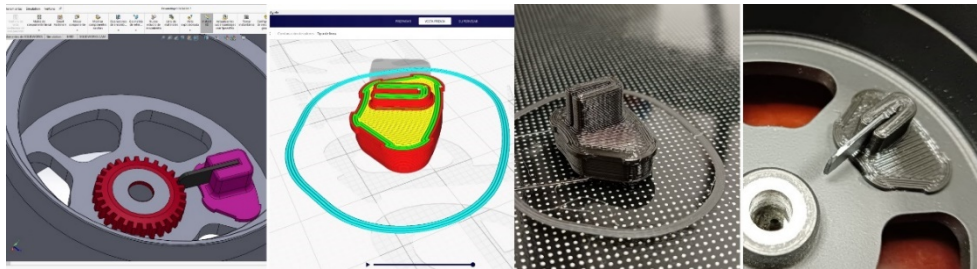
Del diseño a la fabricación del elemento “carraca”: impresión 3D mediante la técnica FDM.
